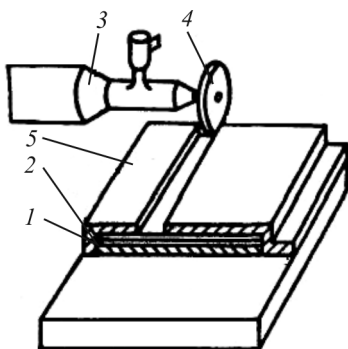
Схема роликовой СТ: 1, 2 – свариваемые заготовки; 3 – шпиндель; 4 – вращающийся ролик; 5 – прижимы
